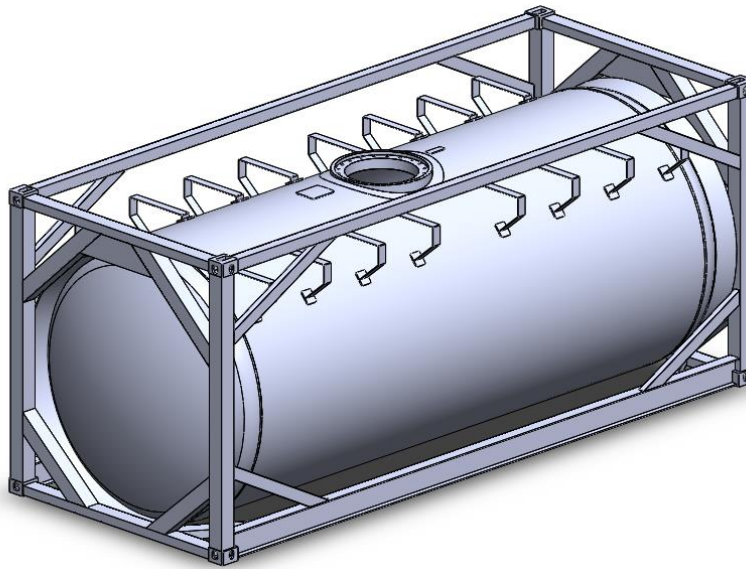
Soportes soldados a la cisterna. Fuente propia.
